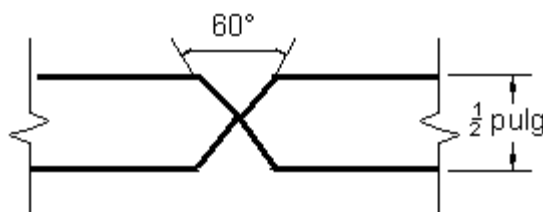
Forma de preparación de la unión para la soldadura
